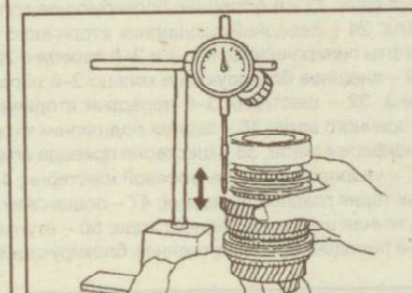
Проверка зазора шестерни 5-й передачи первичного вала
